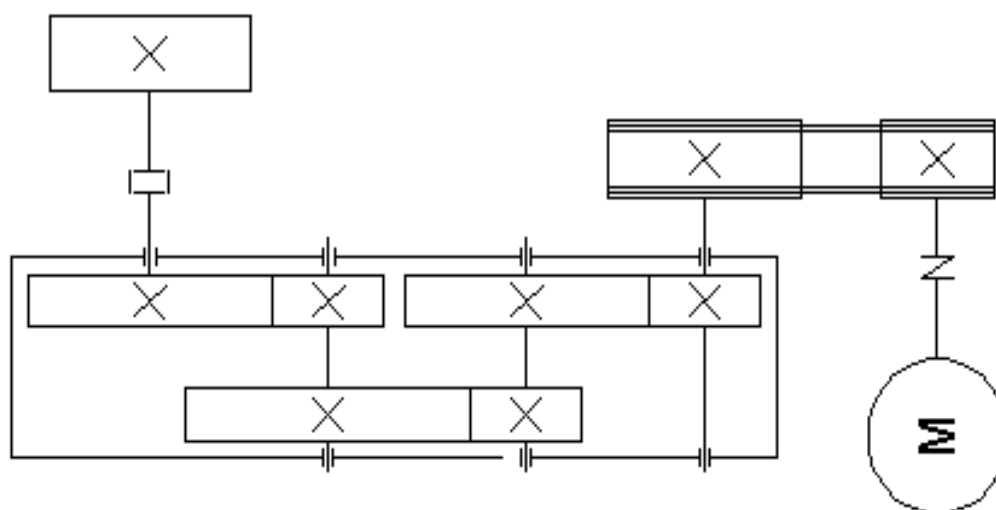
Кинематическая схема привода бутарной бочки
